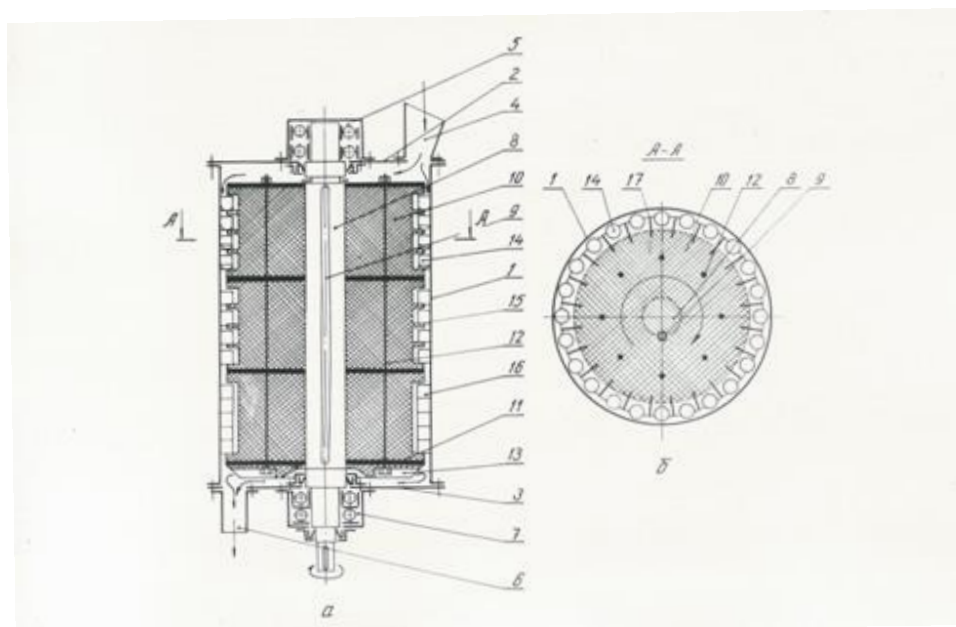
Сема каскадной измельчительной машины центробежного типа МКЦ-4М. 1-корпус мельницы; 2 – крышка верхняя; 3 – нижняя плита; 4 – загрузочный патрубок; 5 – верхний подшипниковый узел; 6 – разгрузочный патрубок; 7 – нижний подшипниковый узел; 8 – вал ротора; 9 – шпонка; 10 – ротор; 11 – разделительный диск; 12 – стягивающие шпильки; 13 – выгребные лопатки; 14, 15, 16 – мелющие тела; 17 – толкающая пластина.
